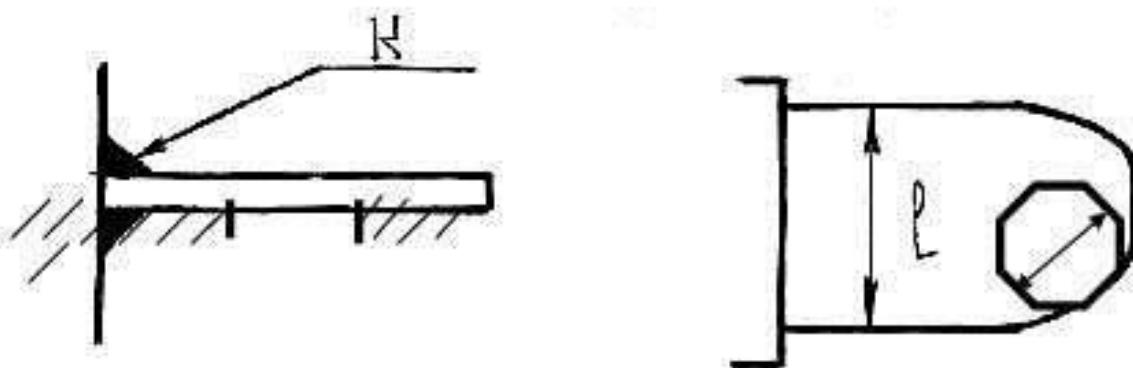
Схема для расчета катета сварного шва
